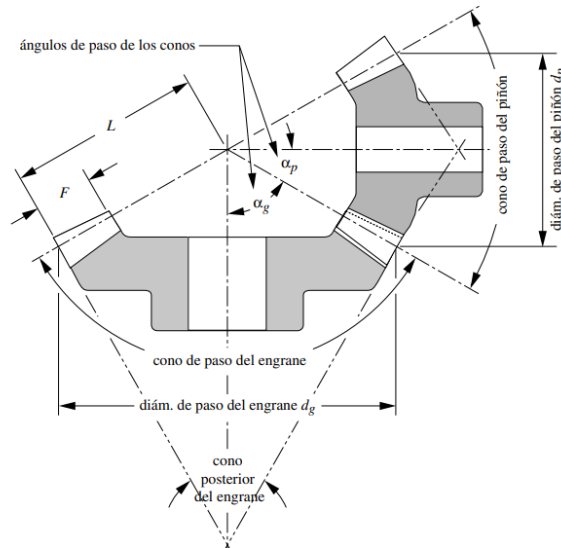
Sección transversal mecanismo de engranajes cónicos [9].
